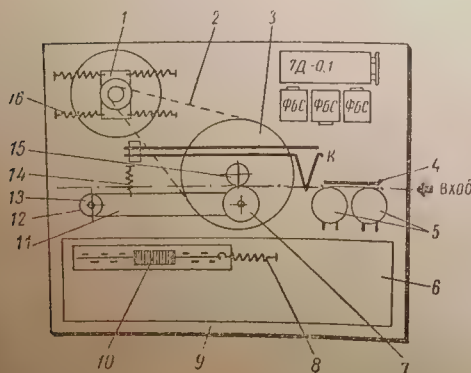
Кинематическая схема репетитора: 1 — двигатель ДП-10; 2 — пассив; 3 — маховик с тоном; 4 — планка-примик; 5 — головки ГУ и ГС; 6 — печатная плата с усилителем; 7 — прижимной ролик; 8 — пружина переключателя; 9 — шасси; 10 — рычаг; 11 — ось; 12 — шуруп; 13 — ось; 14 — рычаг; 15 — ось маховика; 16 — пружинки крепления двигателя.
